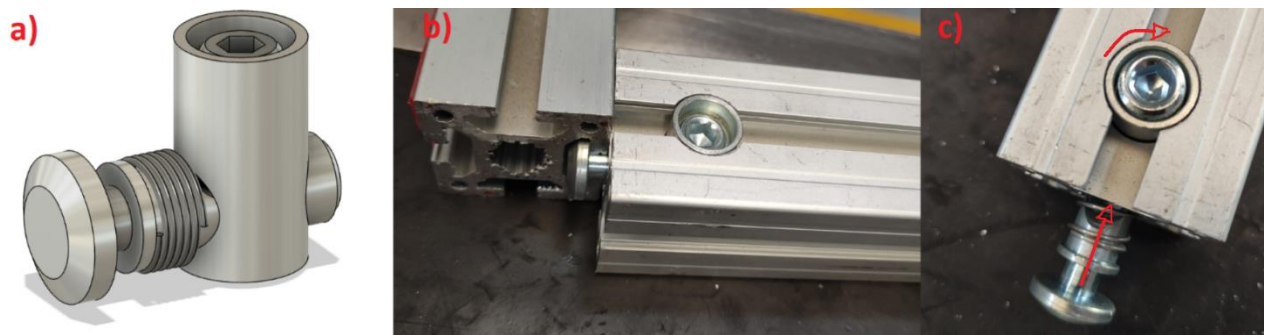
Sistema de unión para perfil ranurado de aluminio 4040 ensamblado.
